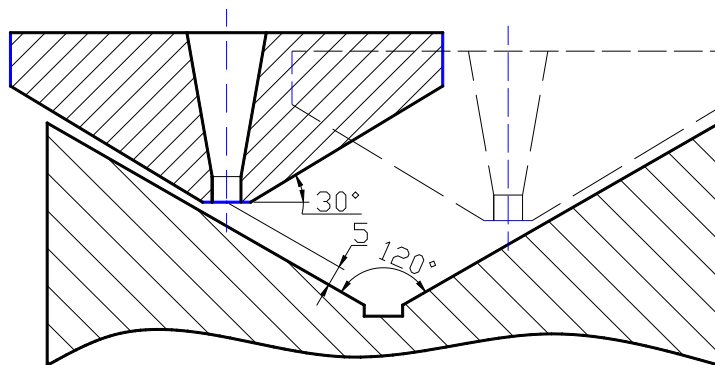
Использование плазмотрона с коническим соплом для обработки направляющих металлорежущих станков
